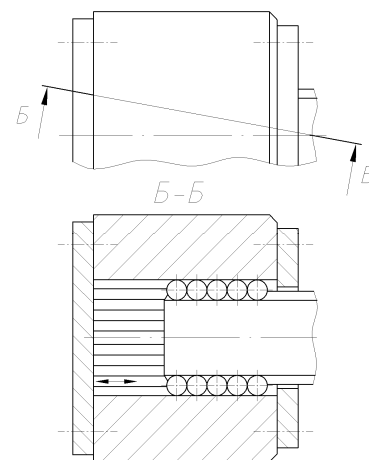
Конструкція кулькового шліцевого з'єднання з нахиленими канавками
